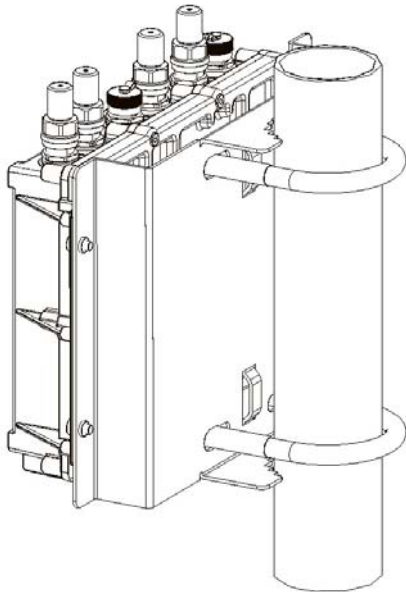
BAT450-F Masthalterungsset mit beigelegten Rundstahlbügeln
